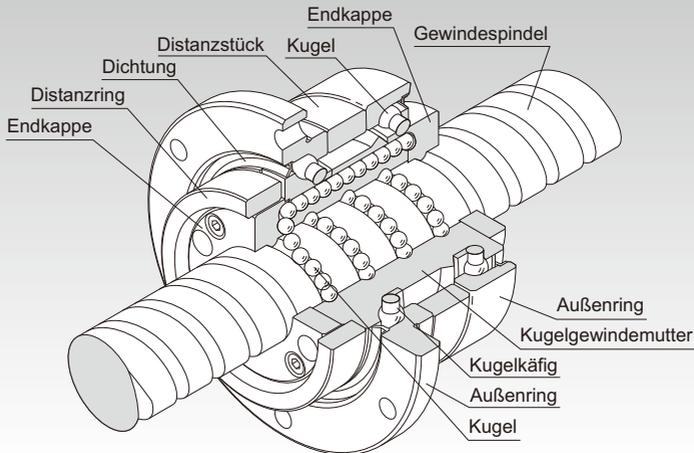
Schnittmodell des Kugelgewindetriebs mit Rotationsmutter und großer Steigung Typ BLR
